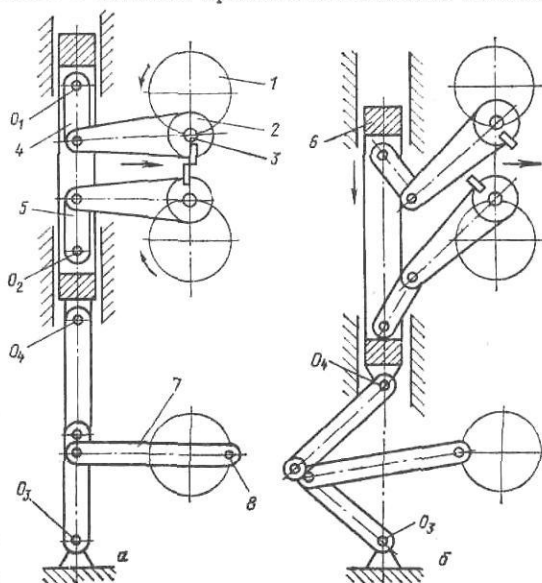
Схема режущего механизма кривошипно-штанговых летучих ножиц со скользящей штангой:
